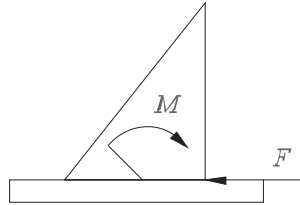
Схема нагружения сварного шва
